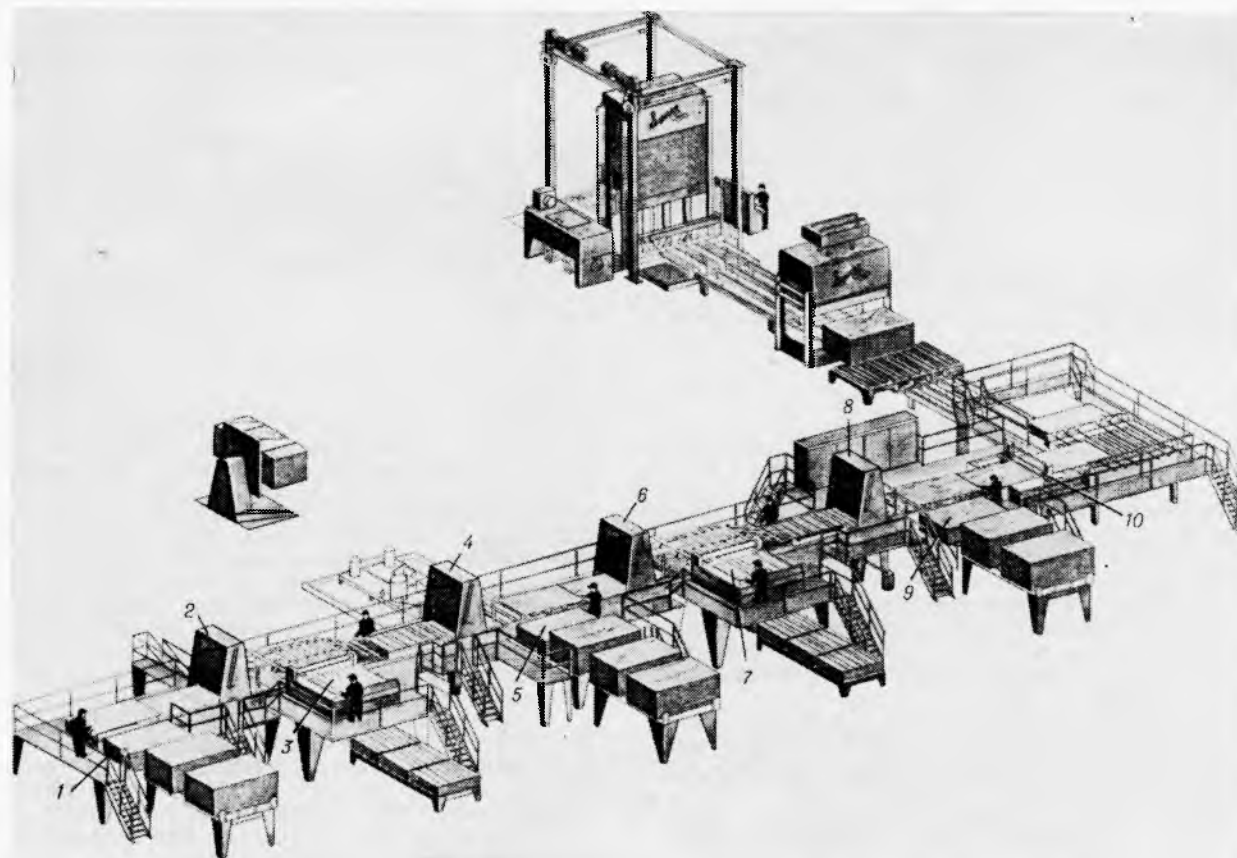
Линия сборки — холодной подпрессовки — склеивания фанеры на базе 40-этажного пресса
